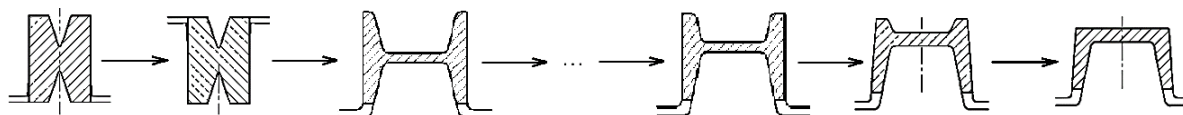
Схема швеллерной калибровки прокатных валков по балочному способу
